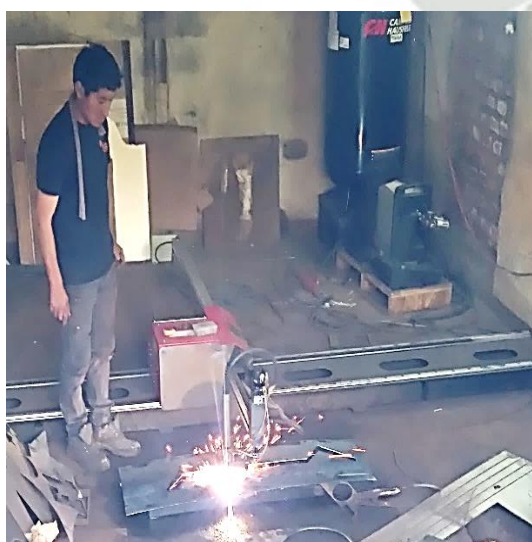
Corte de la plancha de acero para la estructura de soporte del aliviadero escalonado y vista de la estructura base ^{PA}
